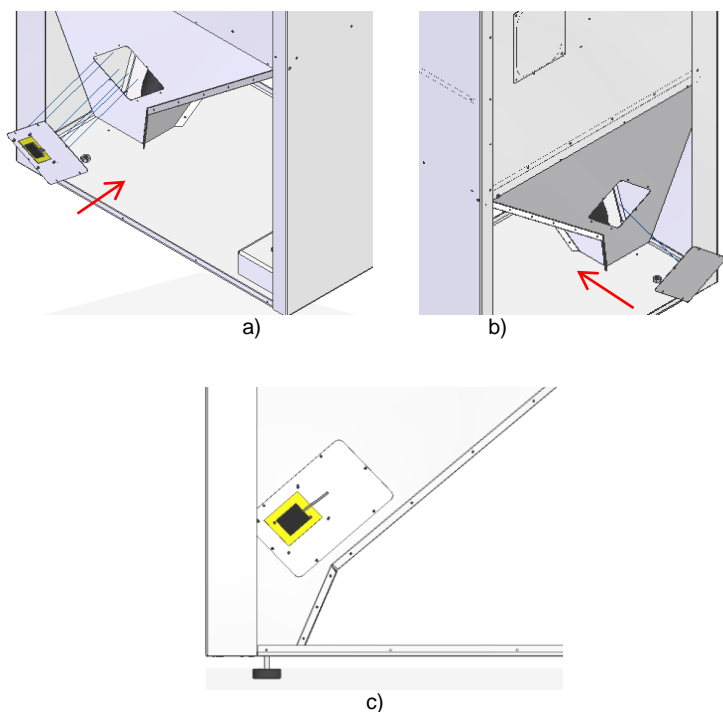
Colocação do sensor de nível de pellets no silo (instalação do silo à esquerda da caldeira)
